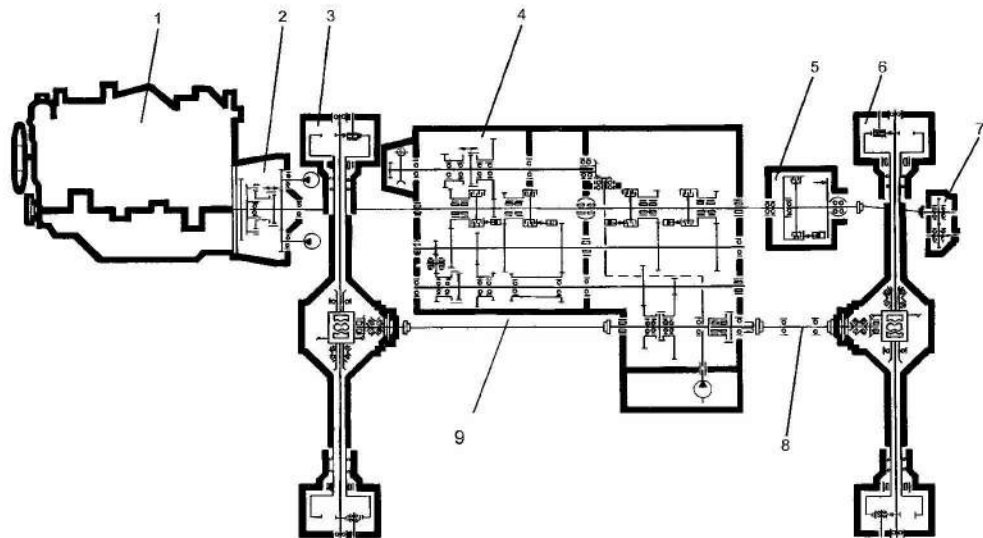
Кинематическая схема трансмиссии: 1 – двигатель; 2 – редуктор с полужесткой муфтой; 3 – передний ведущий мост; 4 – коробка передач; 5 – Соединительная муфта MOM; 6 – задний ведущий мост; 7 – односкоростной редуктор MOM; 8 – опора промежуточная; 9 – карданная передача.
